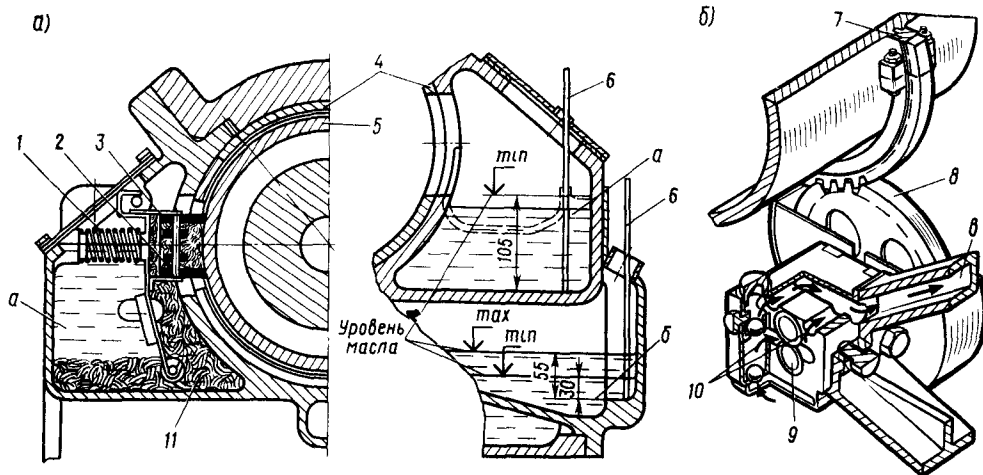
Смазочные устройства моторных подшипников: смазочные камеры (а); шестеренный привод насоса (б):
